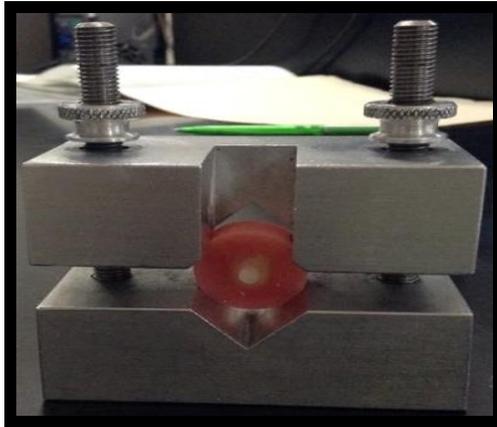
y 21 Prueba montada en aditamento de soporte.
